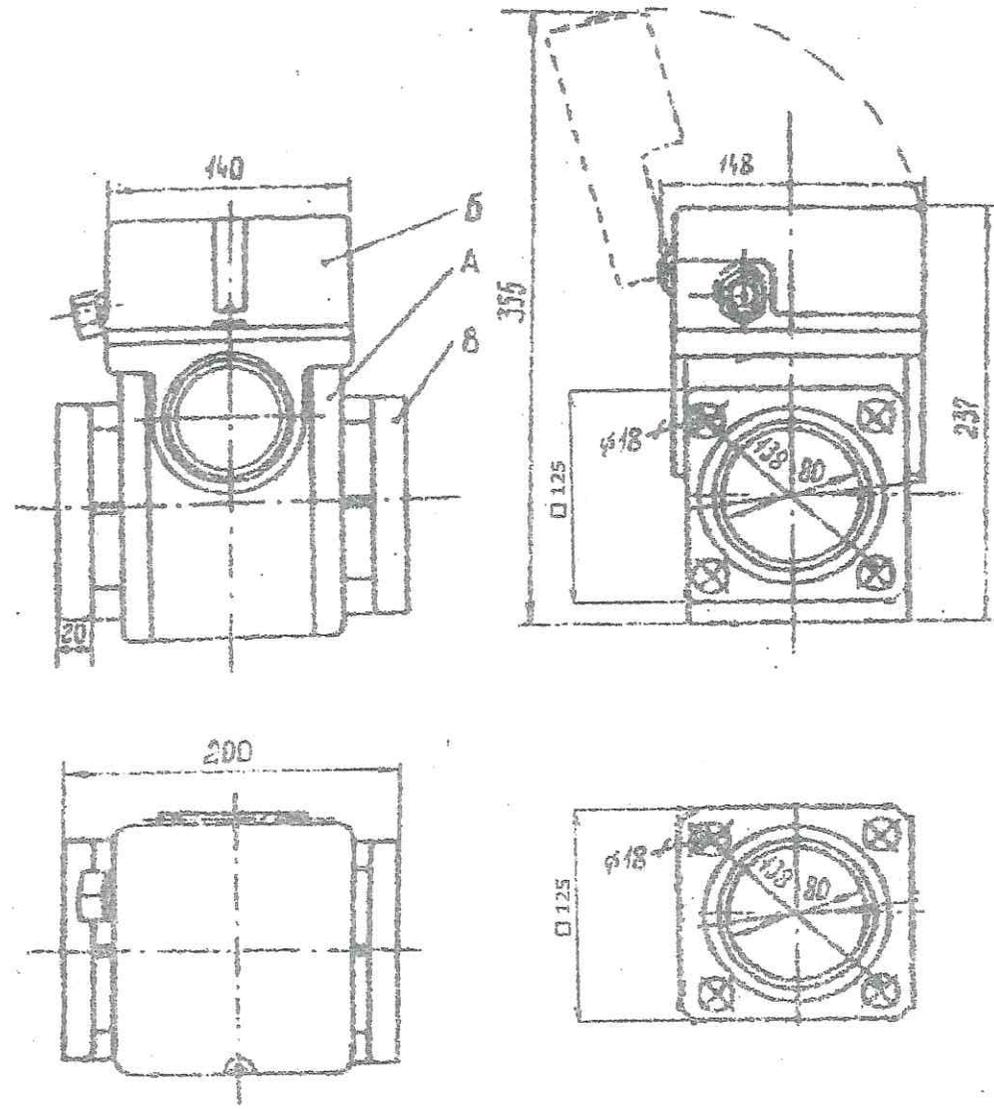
Габаритные и установочные размеры реле РГТ80(50).
